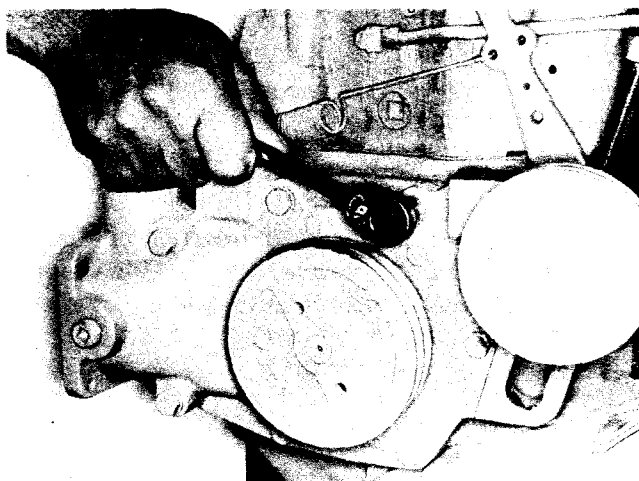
, (N100121). Remoción del conjunto de la bomba de agua.
